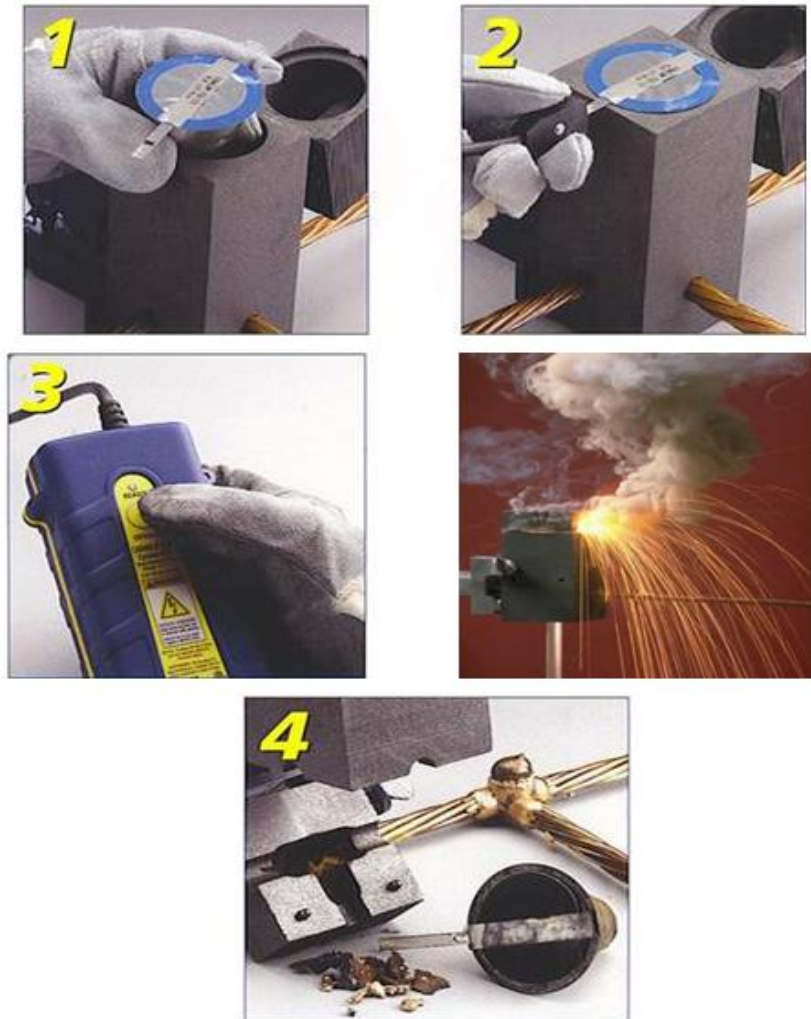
Conexiones eléctricas soldadas permanentes.
